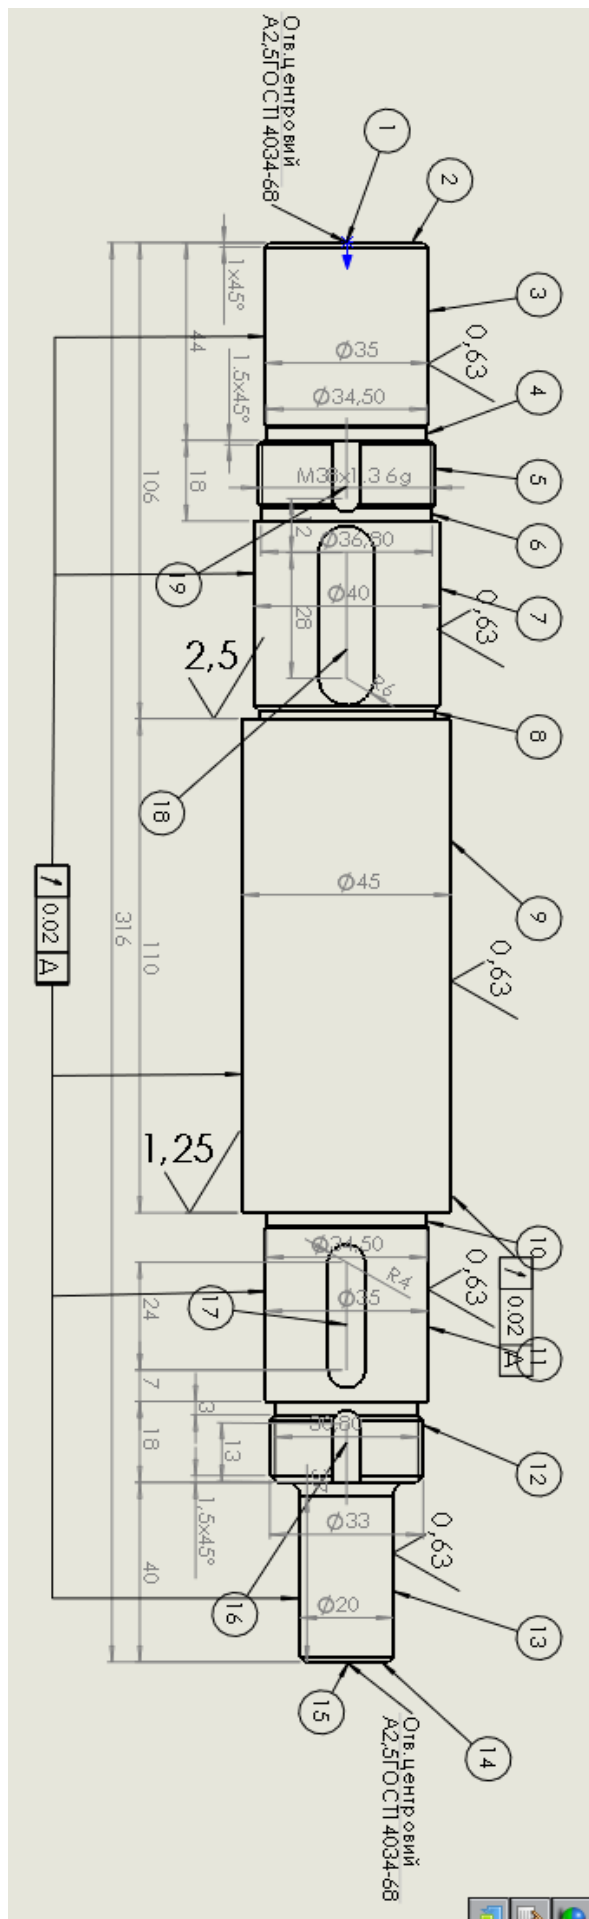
Нумерація поверхонь деталі «Вал».
